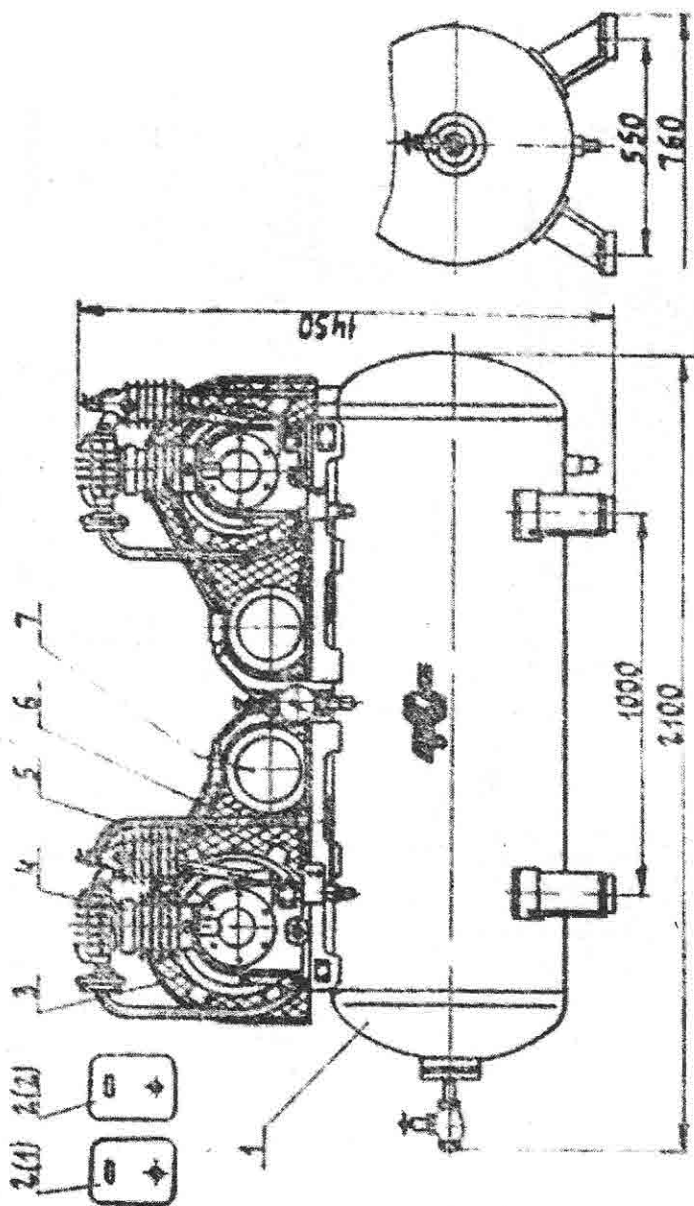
Установка компрессорная, модель К-20 и модель К-30:
